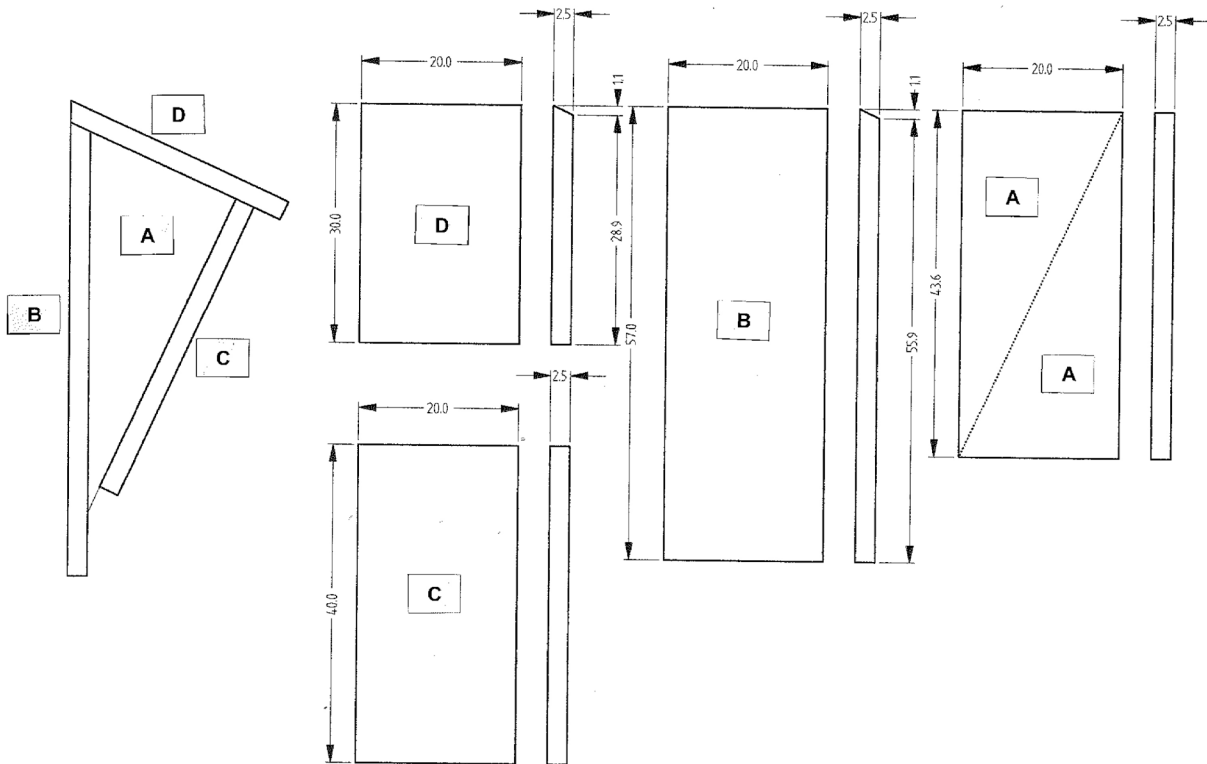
Plano representativo para la construcción de cajas nido para murciélagos de madera de sección triangular.
